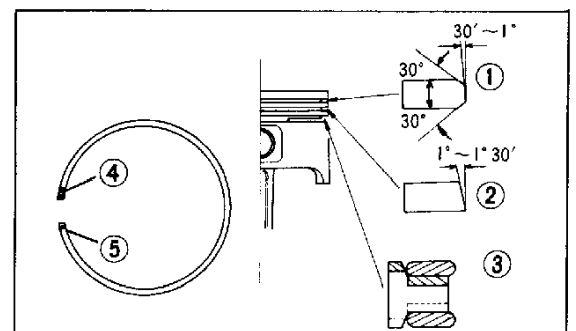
(1) Oberster Kolbenring (4) Firmenbezeichnung
